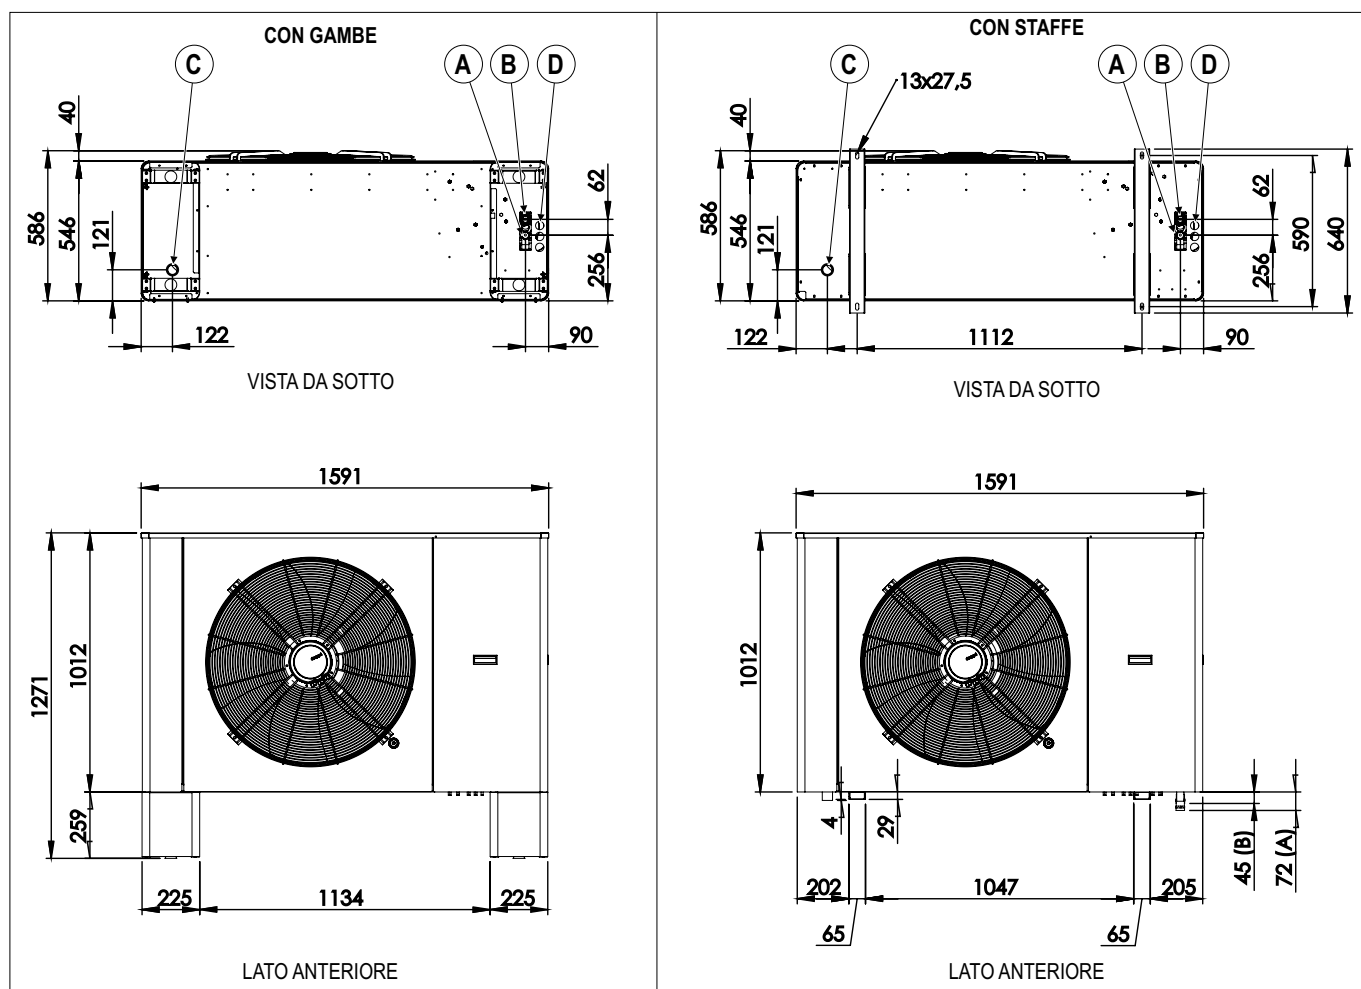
(Dimensioni Serie M - MP - con gambe e con staffe)
